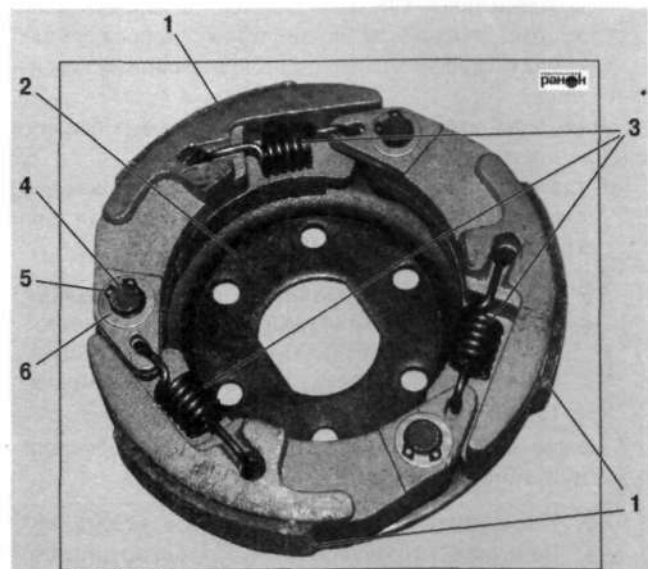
Барабан центробежного сцепления: 1 – колодки сцепления; 2 – основание узла сцепления; 3 – соединительные пружины; 4 – оси колодок сцепления; 5 – стопорные кольца; 6 – прижимные шайбы
